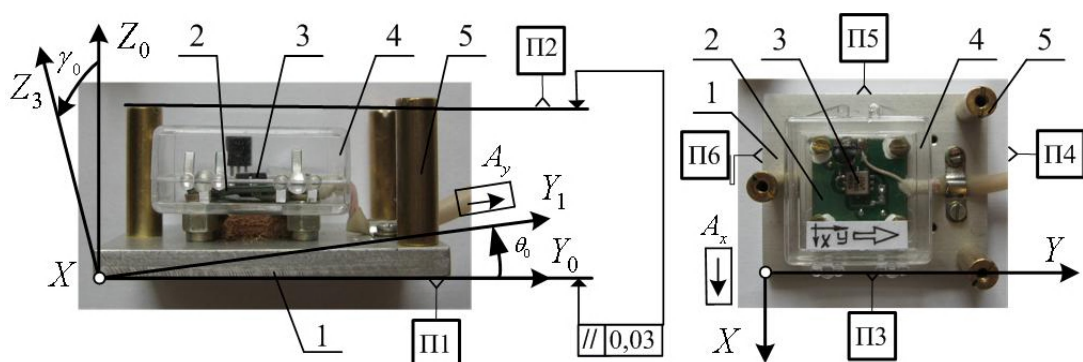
Конструкція ВБ: а) головний вид; б) вид зверху
